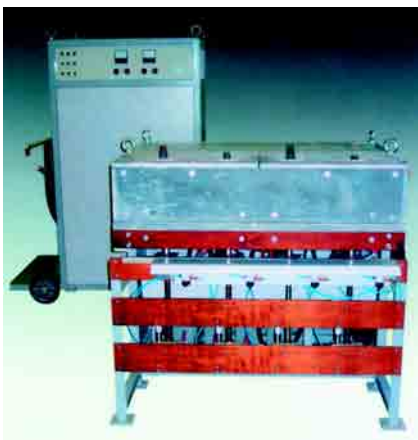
Установка индукционная нагревательная для пайки изделий из твердых сплавов "ЭЛТЕРМ УИП-100-2,4"
